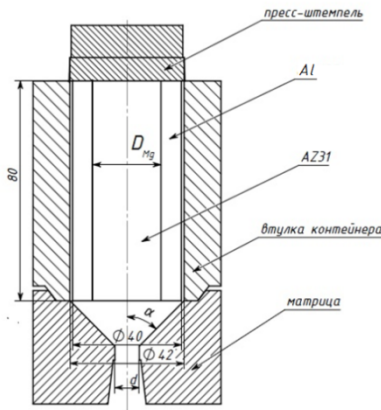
Схематическое изображение сборки инструмента и заготовки
